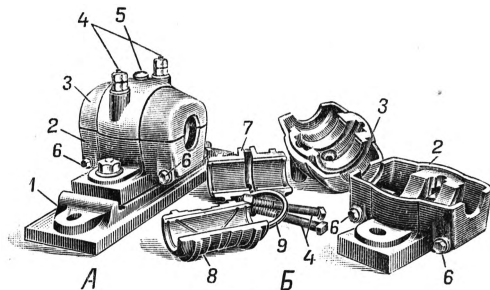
Подшипники скольжения с кольцевой смазкой: А—общий вид, Б—в разобранном виде: 1—плита, 2—нижняя и 3—верхняя части корпуса, 4—болты, 5—пробка, закрывающая отверстие для заливки масла, 6—пробки для слива масла, 7 и 8—части разъемного вкладыша, 9—кольцо для смазки.
